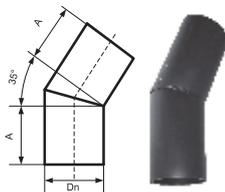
Отвод 35° сварной 2-х сегментный
